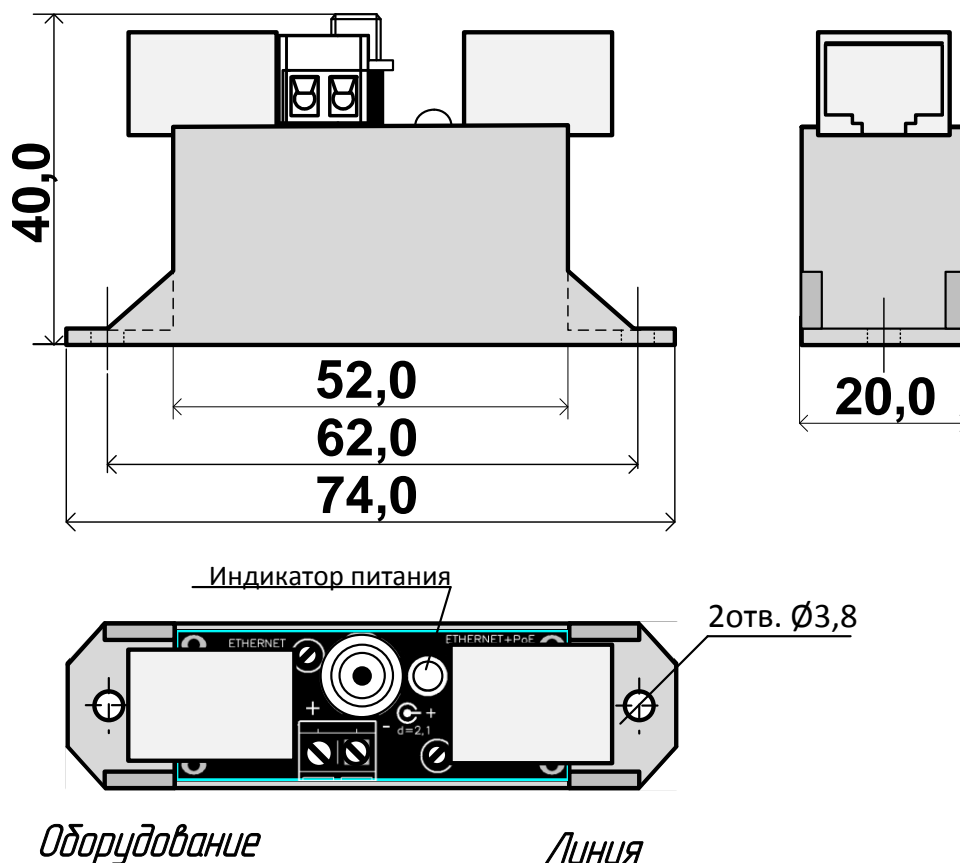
Габаритные и установочные размеры инжектора Commeng PoE IS-B f/f.
